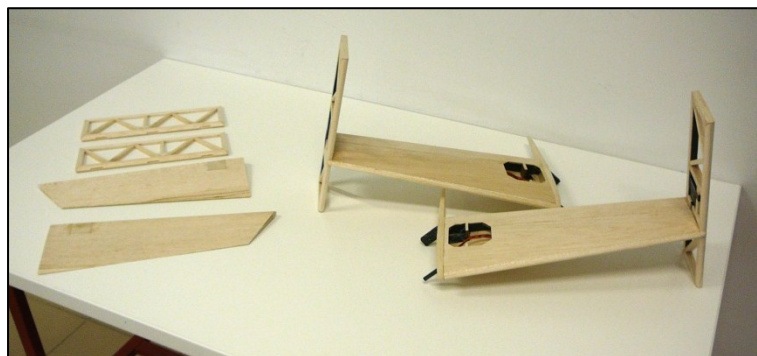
Conjunto de componentes das empenagens H, antes de ser entelado.
